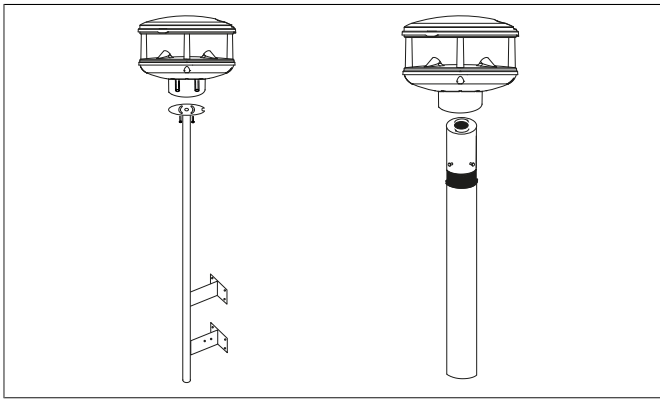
Pose murale sur barre verticale et pose sur mât avec adaptateur \varnothing 50 mm sur barre verticale \varnothing 49 mm
